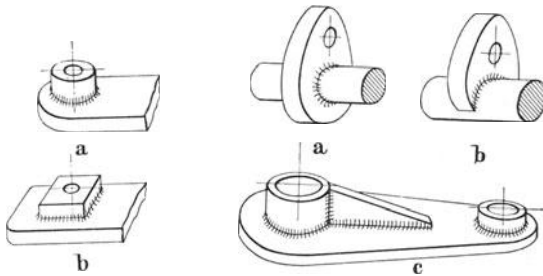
Geschweißte Augen an Hebeln.
